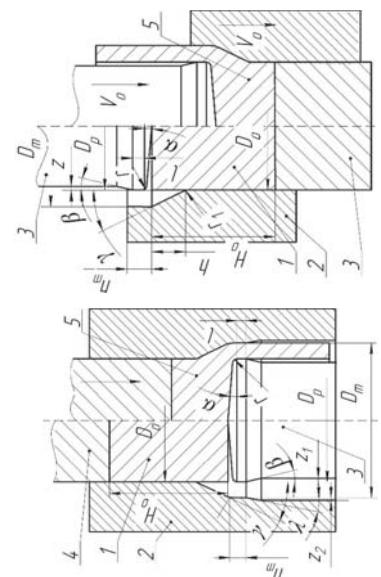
Схеми видавлювання порожністіх виробів: а – пряме видавлювання з роздачою; б – зворотне видавлювання з роздачою
